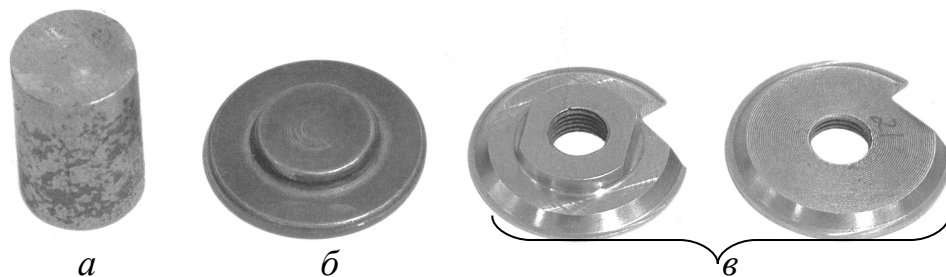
Дисковые резцы из стали Р6М5–МП, полученные в условиях сверхпластического деформирования: *а* – исходная заготовка; *б* – заготовка после СПД; *в* – резцы
